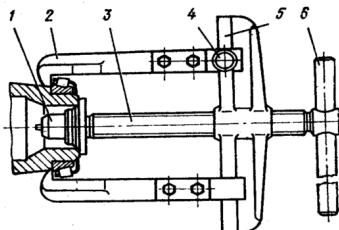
Устройство съемника: 1 – опорная пятка; 2 – захваты; 3 – винт; 4 – фиксаторы захватов; 5 – траверса; 6 – вороток
